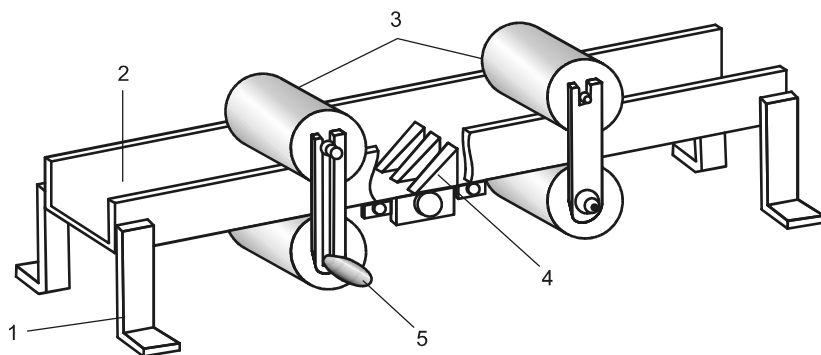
Приспособление для резки резины: 1 — ноги основания; 2 — основание; 3 — ролики; 4 — нож для резки резины; 5 — ручка
